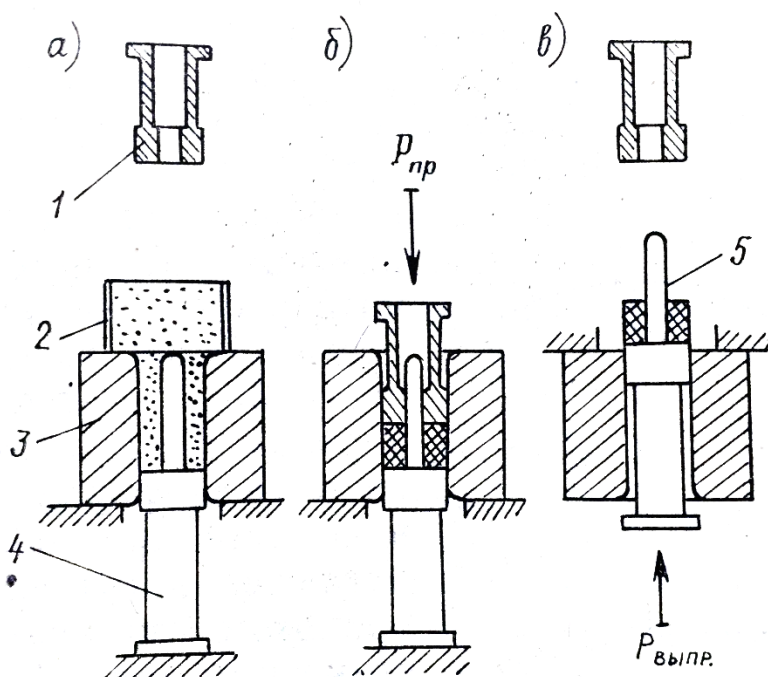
Схема одностороннего прессования: а - засыпка порошковой смеси; б - матрицу прессование верхним пуансоном смеси в изделие; в - выпрессовка заготовки нижним пуансоном; 1- верхний пуансон; 2- питатель; 3 - матрица; 4 - нижний пуансон; 5 – стержень
